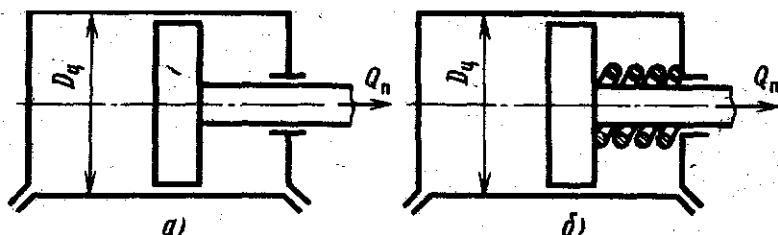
Схема пневматического привода зажима одностороннего (а) и двустороннего (б) действия станочного приспособления
